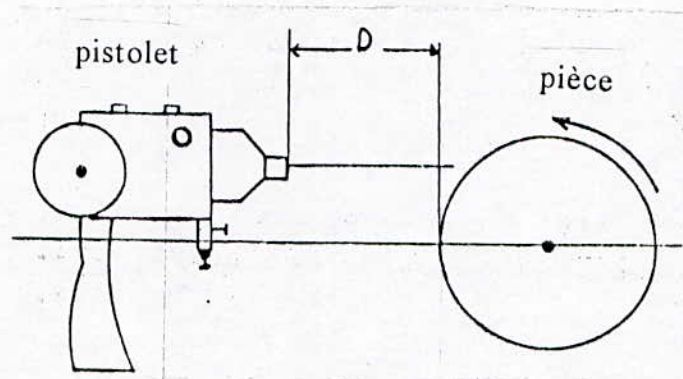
Position du pistolet de projection par rapport à la pièce à recharger.
